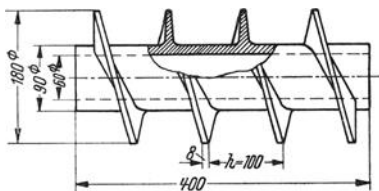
Eingängige Förderschnecke (Werkzeichnung).  $h$  = Steigung oder Ganghöhe.
